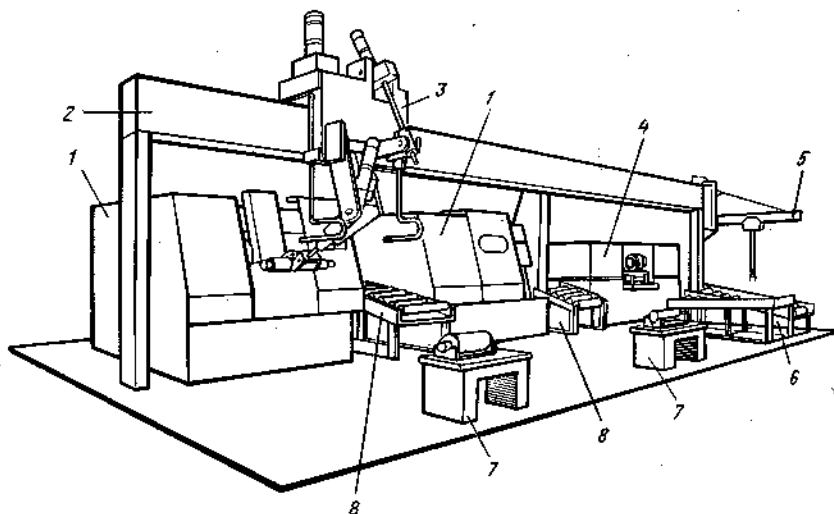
РТК для механической обработки деталей типа тел вращения:
